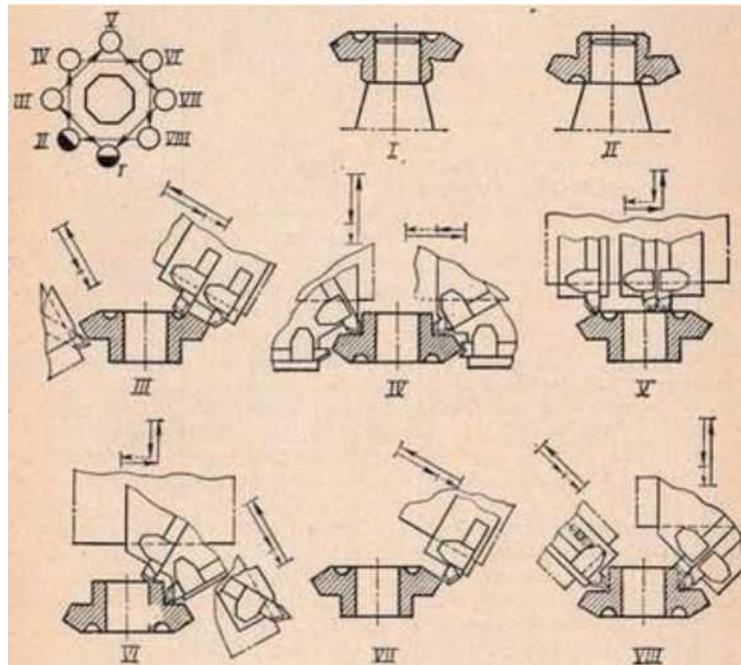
Схема обробки заготовки зубчастого колеса класу «втулка»
